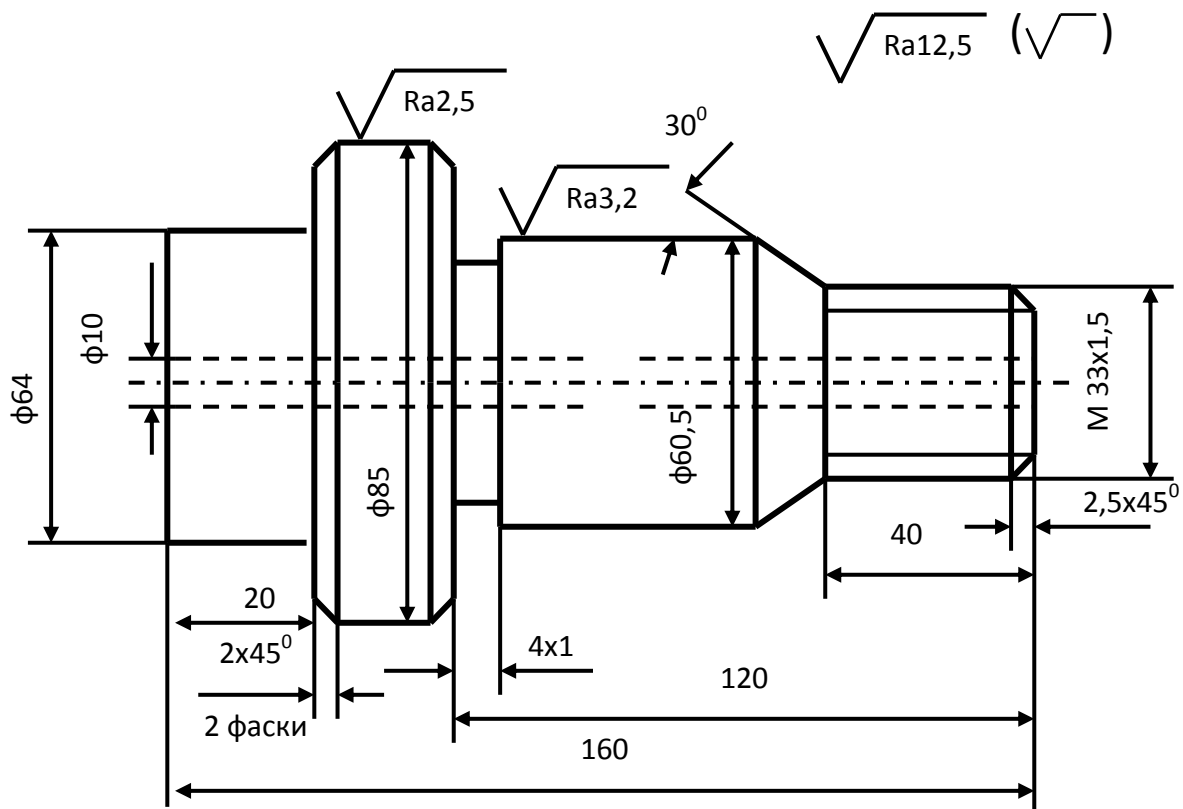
Чертеж токарной заготовки (оформляется на формате А4)
